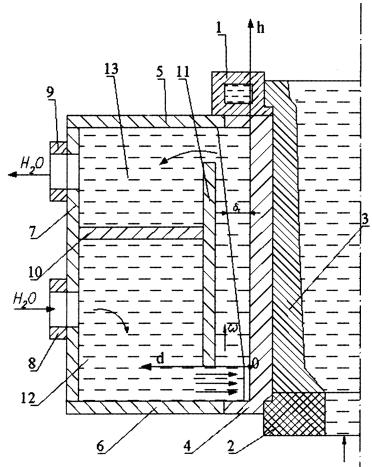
Работа обычного кристаллизатора: I — подвижный кристаллизатор; 2 — соединительный стакан; 3 — отливка; 4 — рубашка; 5 — верхний фланец; 6 — нижний фланец; 7 — корпус; 8 — подводящий патрубок; 9 — отводящий патрубок; 10 — перегородка; 11 — экран; 12 — нижний коллектор; 13 — верхний коллектор
